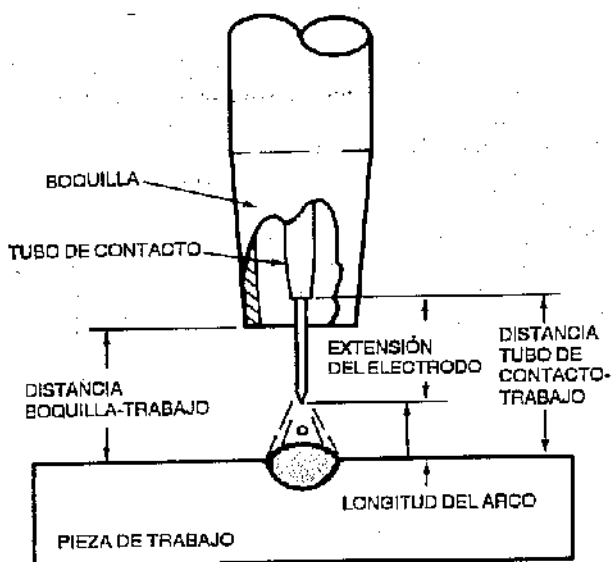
Terminología de soldadura por arco de metal y gas
